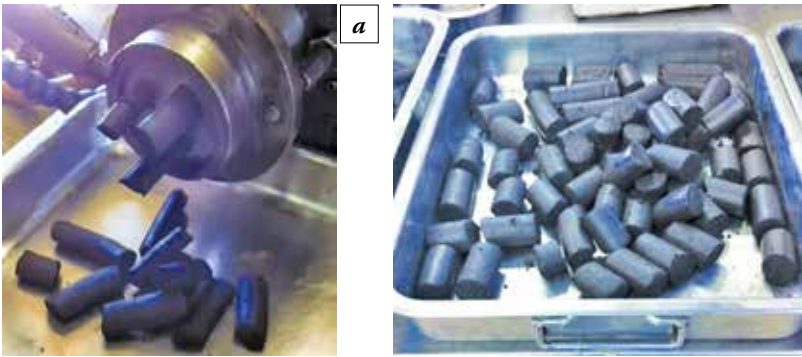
Образцы брэсков: *а* – изготовление брэсков; *б* – внешний вид рудоугольных брэсков
